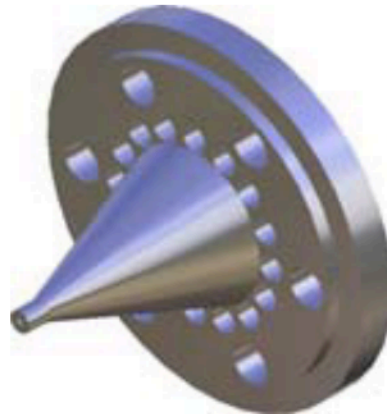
Vista en isométrico del mandril con un soporte con barrenos.
